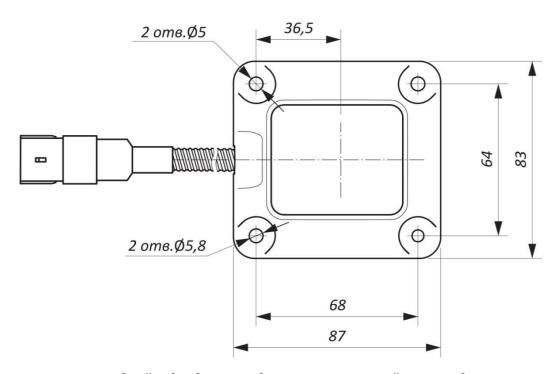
Общий вид изделия, L – длина измерительной части изделия
